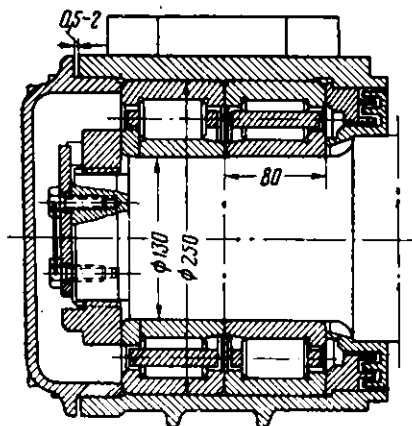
Букса с двумя цилиндрическими подшипниками на горячей посадке
